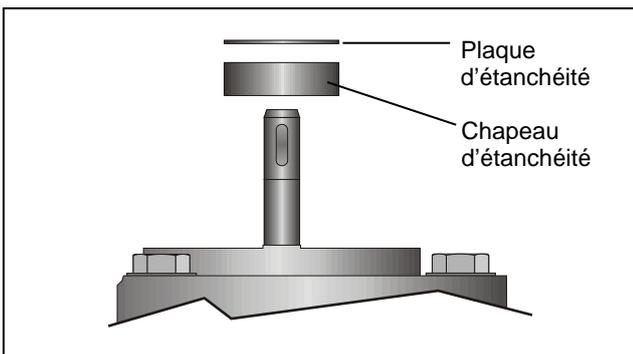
Retrait de la plaque d'étanchéité et du chapeau d'étanchéité
